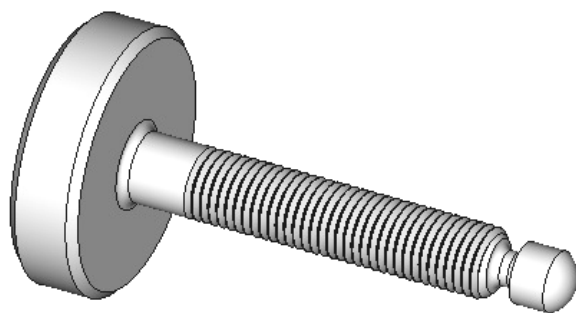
Винт нажимной для непосредственного контакта с заготовкой
